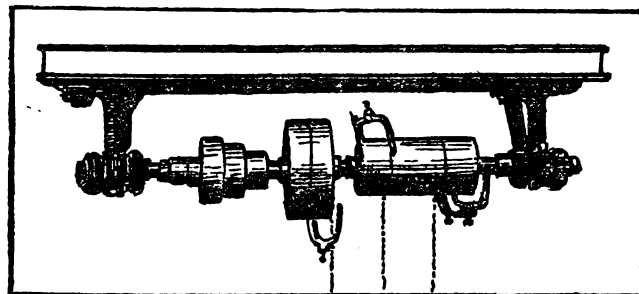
Приводно-шлифовальный станок на роликовых подшипниках.
